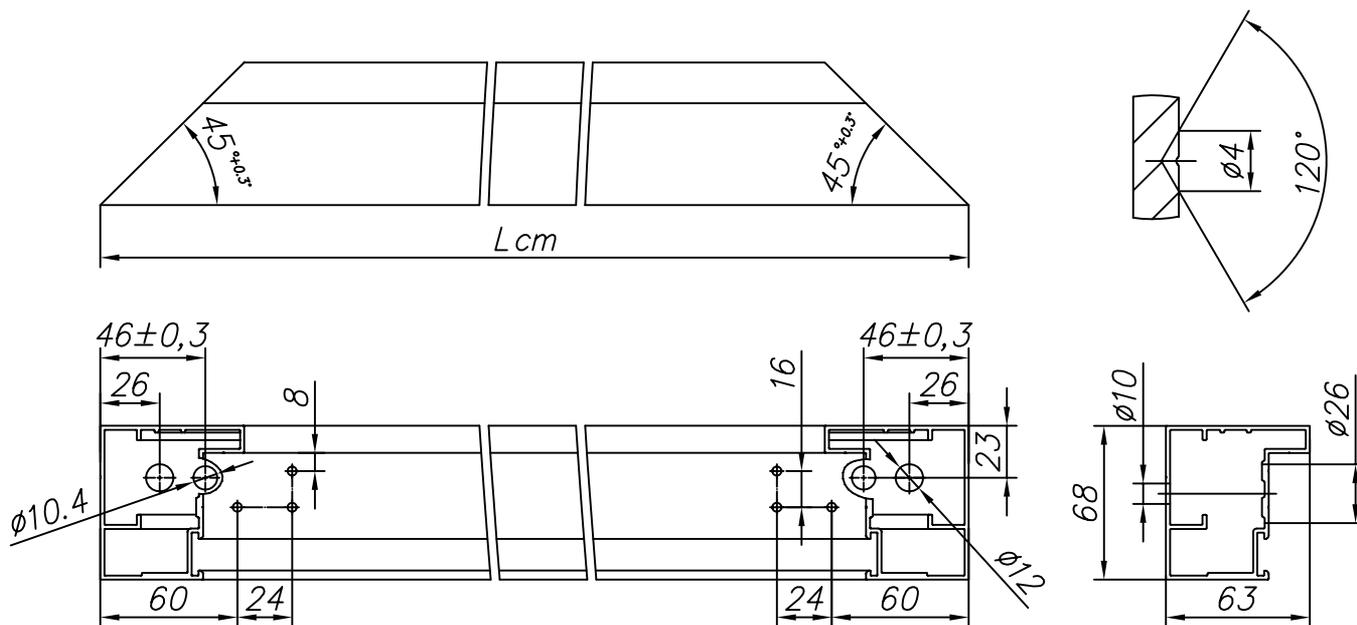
Изготовление стойки из профиля FLGU.400.0107 (для накладного монтажа)
